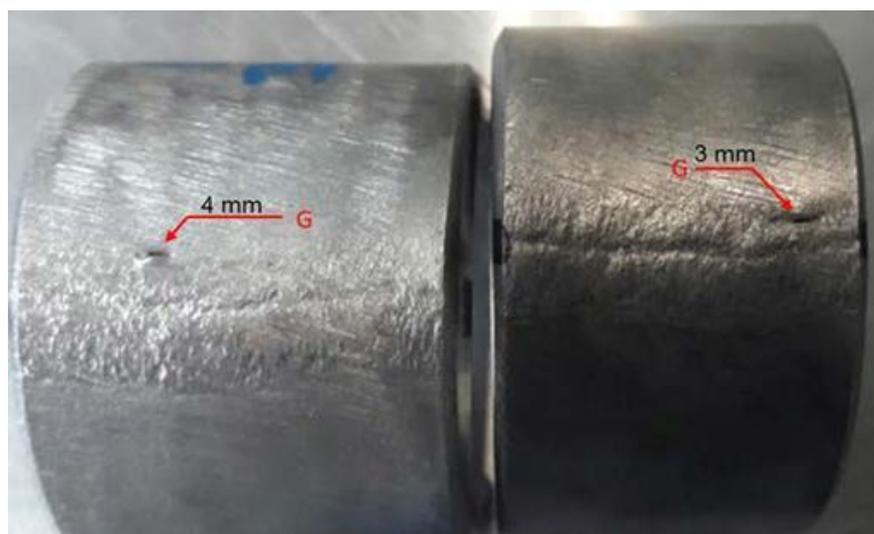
Probetas soldadas – Ensayo de doblez de cara.
